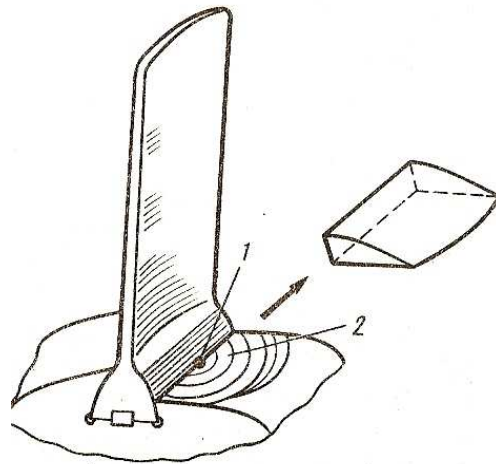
Схема усталостного разрушения диска компрессора ГТД от фреттинг-коррозии: 1- очаг фреттинг-коррозии; 2- зона развития трещины усталости
